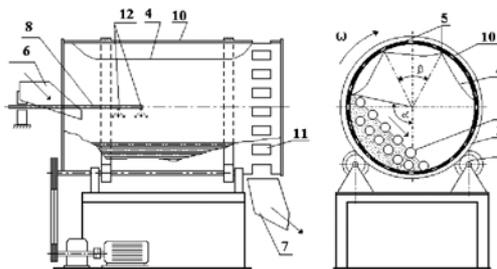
Схема барабанного смесителя с независимыми рабочими органами типа "стержни-катки": 1- привод смесителя, 2- корпус. 3- катки опорные. 4- эластичный материал, 5- крепление эластичного материала к корпусу, 6- загрузочный лоток, 7- разгрузочный лоток. 8- трубоводы для подачи жидких компонентов. 9- стержни-катки, 10- вентиляционные отверстия, 11- разгрузочные отверстия. 12- распылители жидких компонентов.
